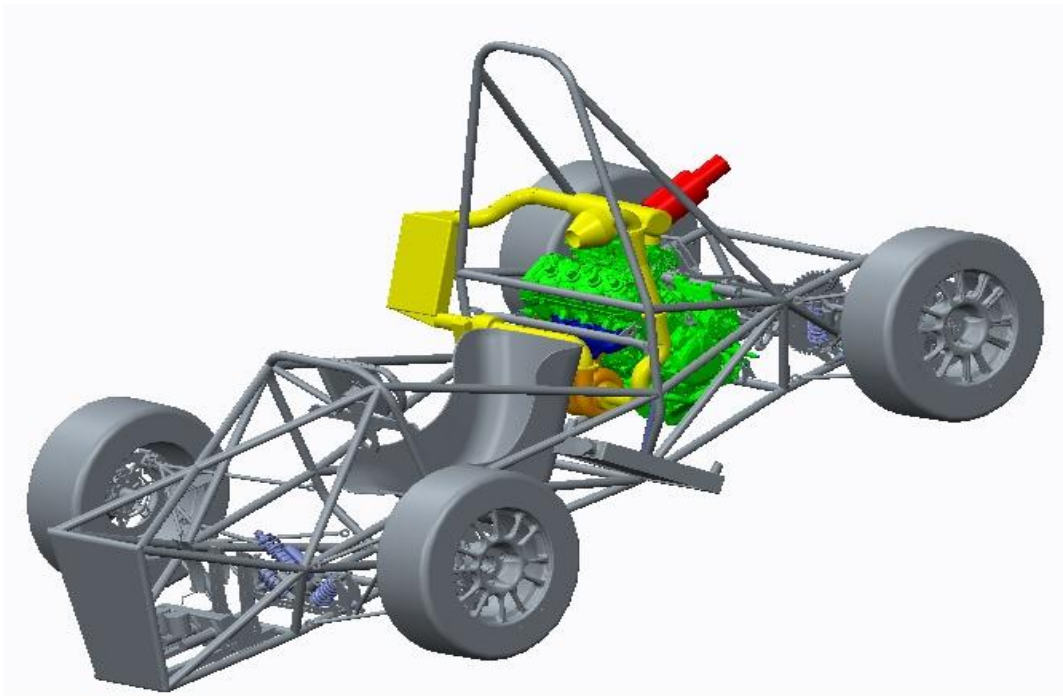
Model sestavy motoru GSX-R600 s přeplňováním.
